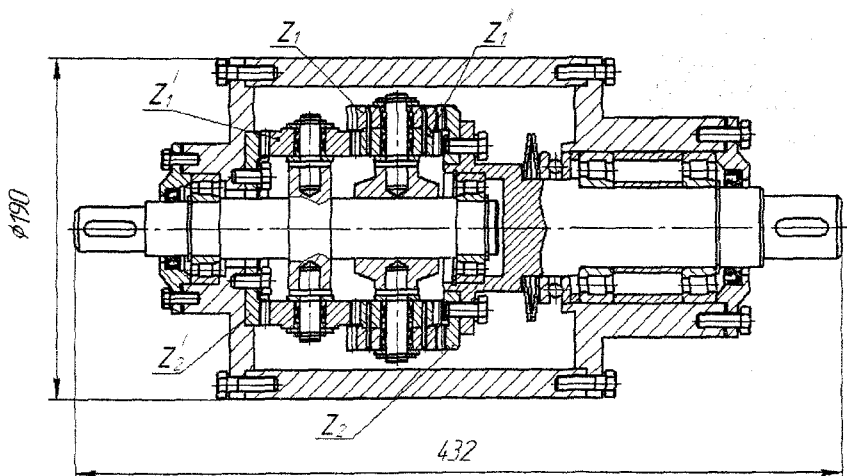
Осевой разрез планетарного редуктора с плоскоколесными передачами
